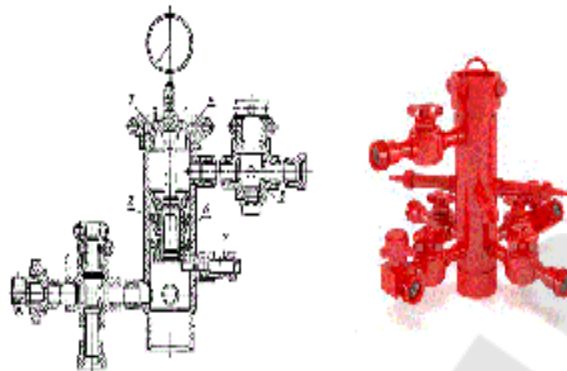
Головка цементи́ровочная универсальная ГЦУ: 1 – обвязка; 2 – корпус; 3 – крышка; 4 – накидная гайка; 5 – пробковый кран; 6 – цементная пробка; 7 – стопорный винт
